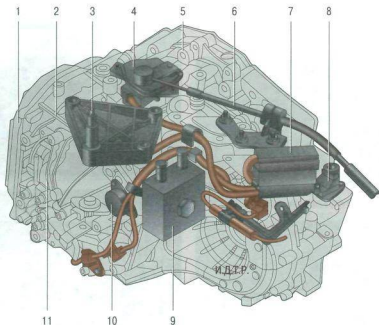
Автоматическая коробка передач: 1 – крышка блока клапанов; 2 – картер планетарного редуктора; 3 – кронштейн левой опоры подвески силового агрегата; 4 – комбинированный многофункциональный переключатель выбора режимов; 5 – картер гидротрансформатора; 6 – трос управления коробкой передач; 7 – электронный блок управления; 8 – датчик скорости; 9 – теплообменник рабочей жидкости; 10 – клапан управления расходом жидкости через теплообменник; 11 – задняя крышка планетарного редуктора
